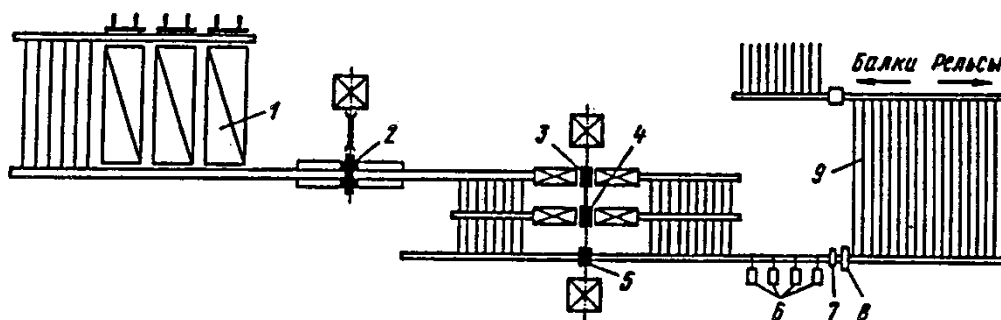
Схема расположения оборудования рельсобалочного стана:
